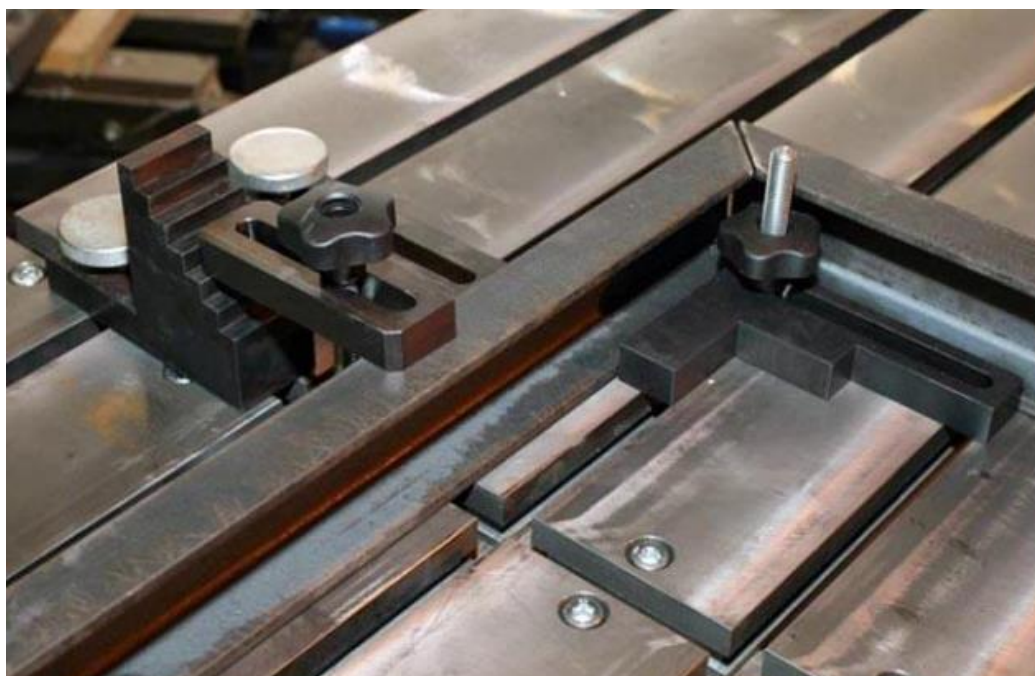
Схема фиксации деталей при сварке
